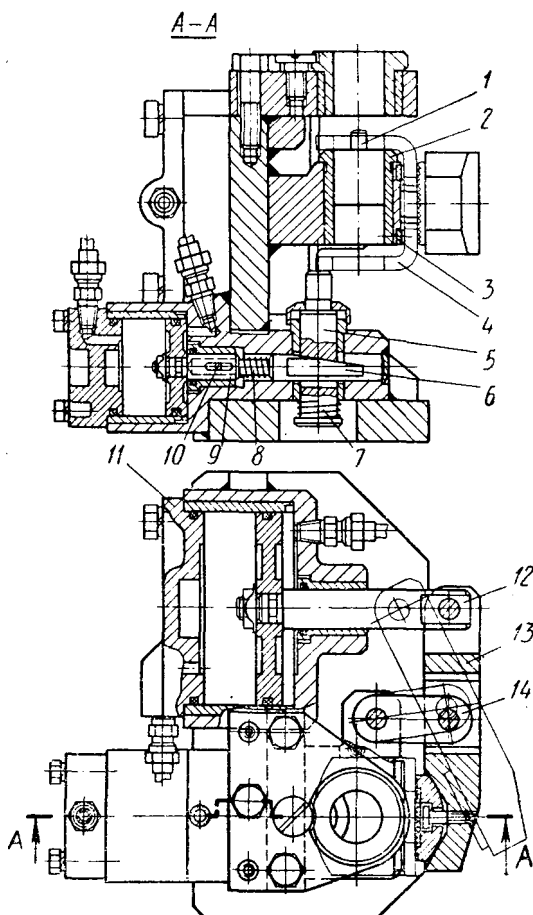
Пневматическое приспособление с дополнительной опорой для обработки вилок и серег на вертикально-сверлильном станке
